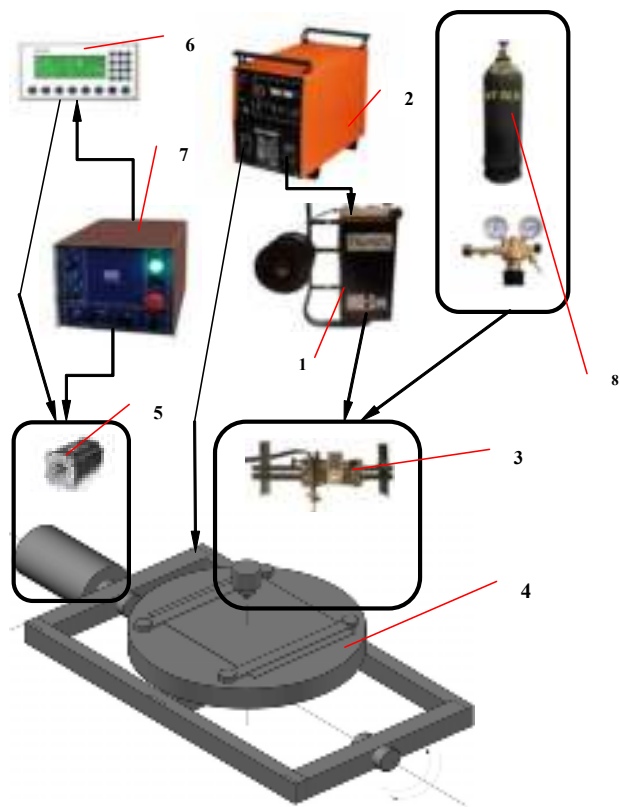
Установка для наплавки в среде углекислого газа с колебаниями сварочной ванны: 1 – полуавтомат сварочный; 2 – источник питания сварочной дуги; 3 – сварочная горелка и механизм её перемещения; 4 – подвижный стол с закреплённой деталью; 5 – шаговый двигатель; 6 – пульт управления шаговым двигателем; 7 – блок управления шаговым двигателем; 8 – баллон с углекислым газом
